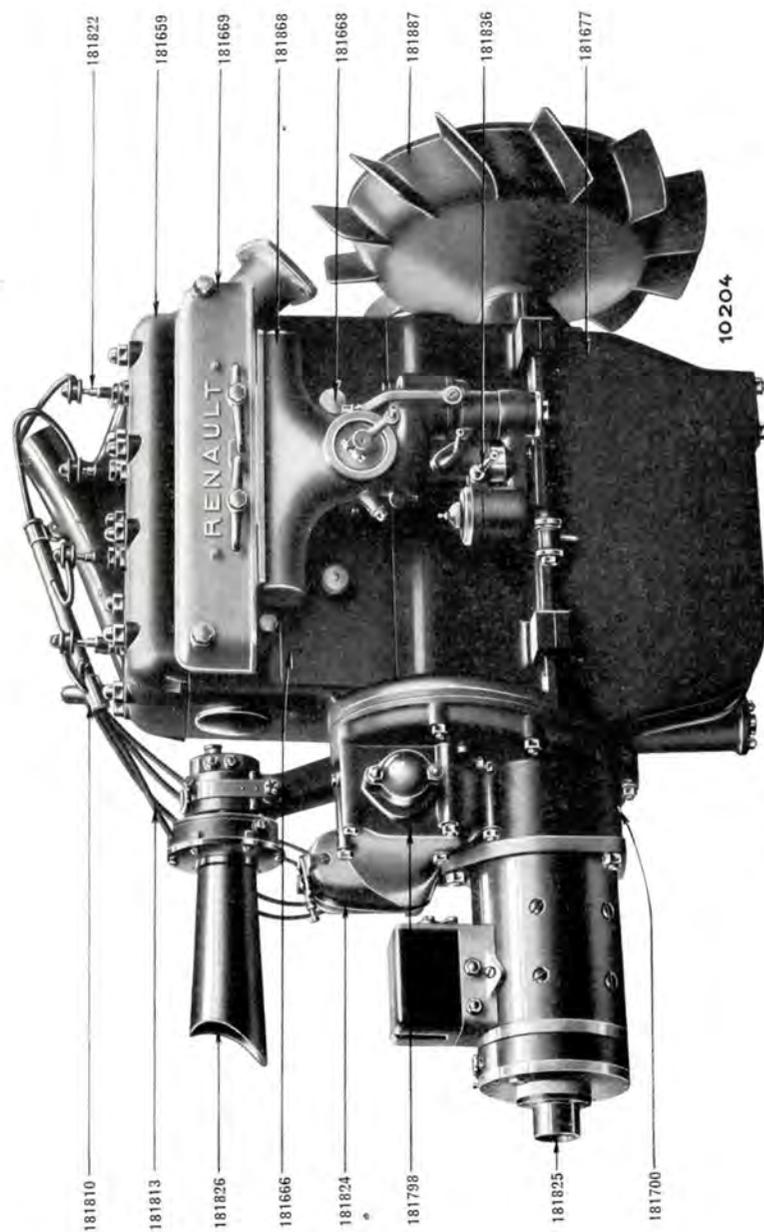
Le moteur. Vue extérieure, côté carburateur.
